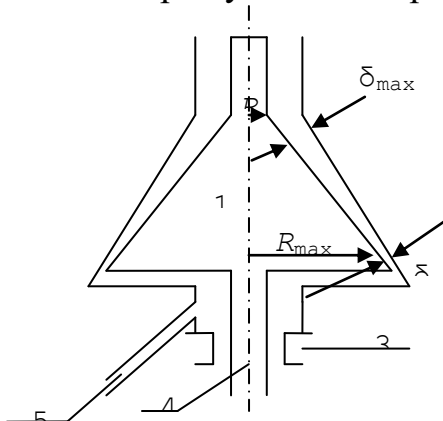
Схема коллоидной мельницы с переменной величиной зазора: 1 – ротор, 2 – статор, 3 – подшипник вала 4, 5 – выходной патрубок для приготовления эмульсии
